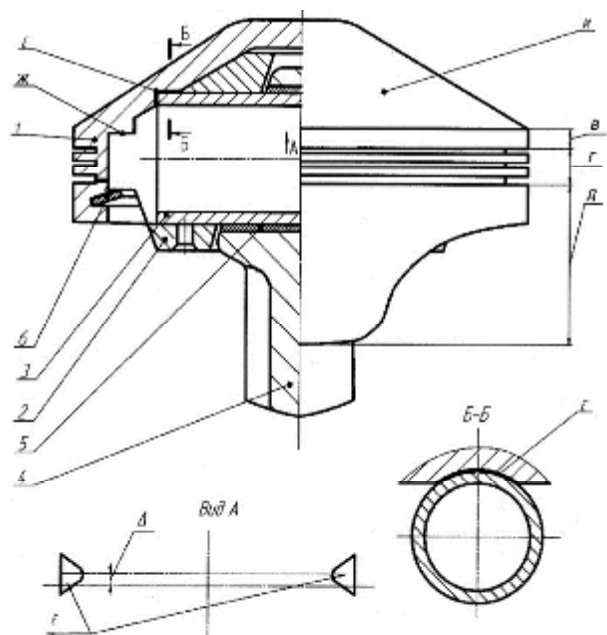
Поршень двигуна внутрішнього згоряння з тонкостінним корпусом; 1 – корпус оболонковий, 2 – вставка, 3 – палець поршневий; 4 – шатун; 5 – мідна втулка; 6 – тарільчасте кільце.
